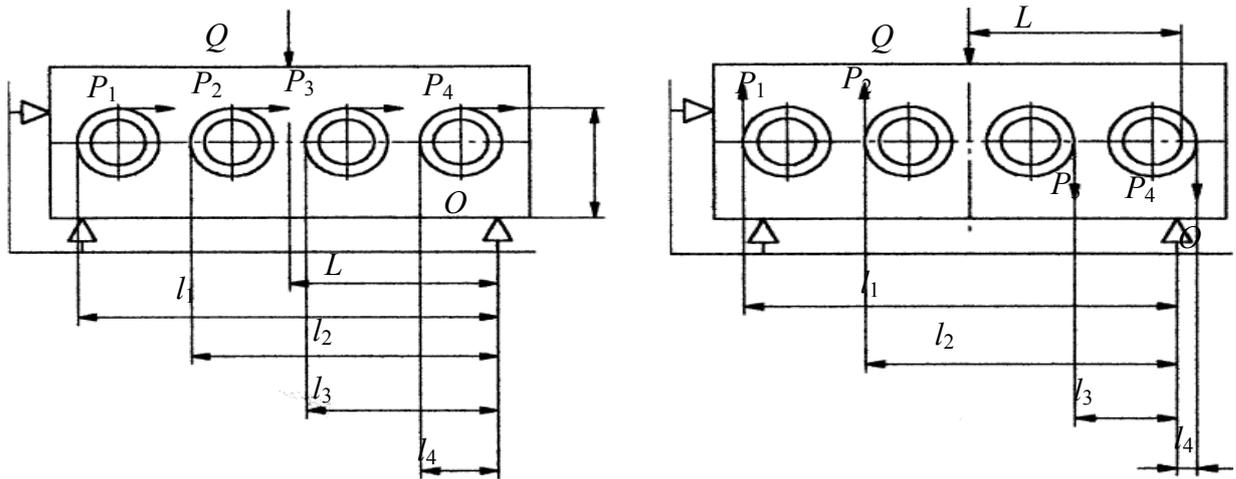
Схемы для расчета сил закрепления заготовок при многоинструментальной обработке
